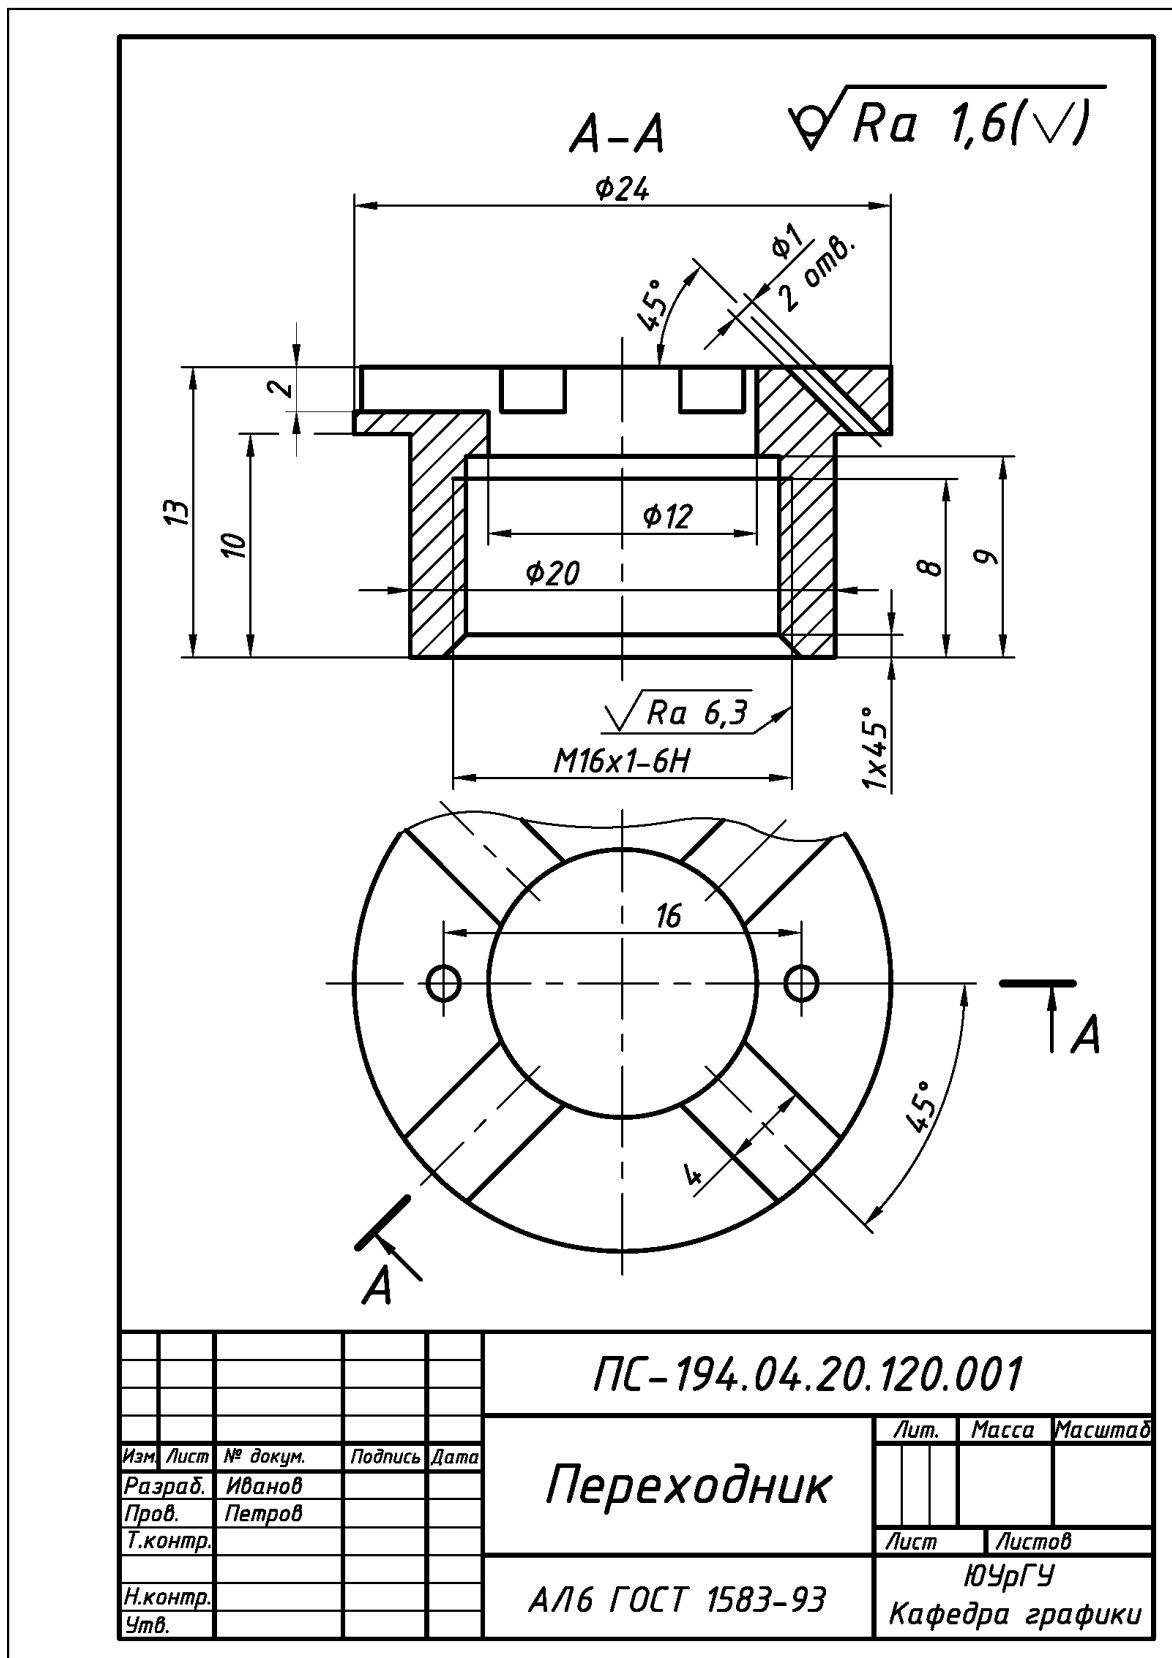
Пример выполнения и оформления эскиза детали «Переходник», изготовленной из сплава литьем под давление и прочисткой резьбы
